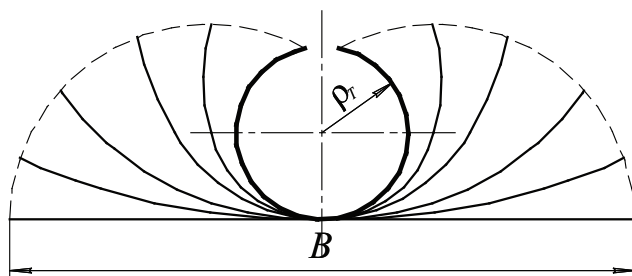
«Цветок» формовки для однорADIUSной калибровки
